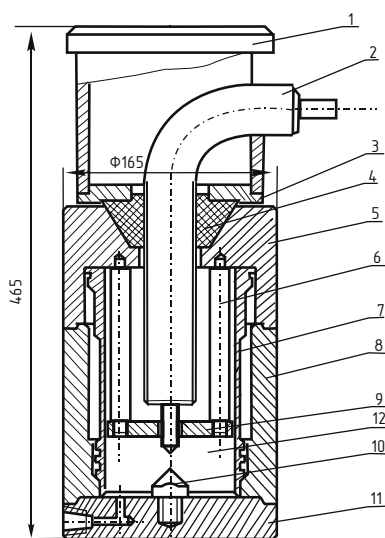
Приспособление для раздачи гильзы цилиндра двигателя ЗИЛ-5301: 1 – стакан; 2 – электрод; 3 – фланец; 4 – гайка; 5 – крышка; 6 – стойка; 7 – гильза цилиндра; 8 – обойма; 9 – отражатель; 10 – электрод; 11 – основание; 12 – камера.
